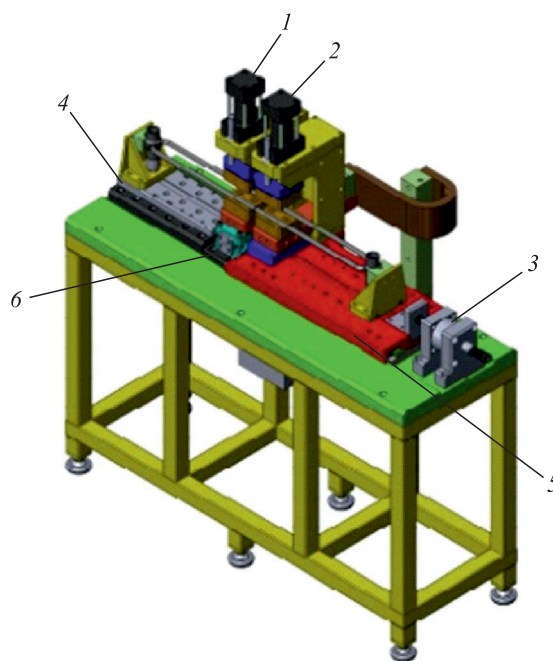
Общий вид двухкоординатного станка сварки закладных: 1 – цилиндр блокиратора левой половины; 2 – цилиндр блокиратора правой половины; 3 – цилиндр прижима правой половины; 4 – ложемент левой половины; 5 – ложемент правой половины; 6 – сварочный коллектор
